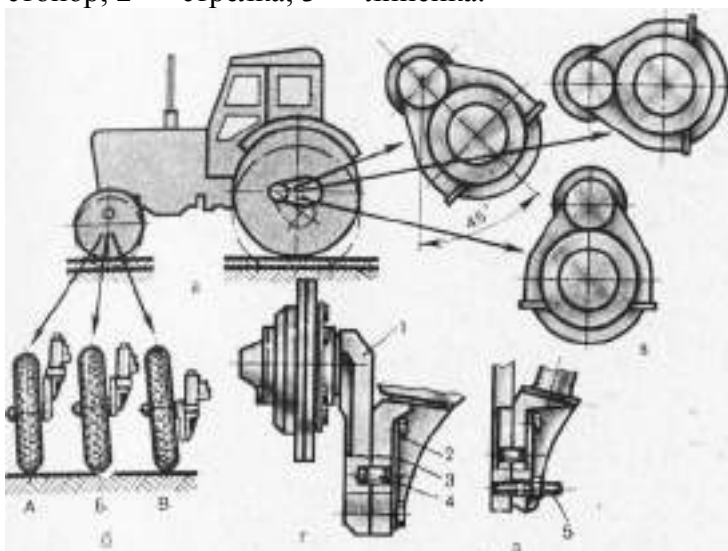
Ходовая часть универсально-пропашного трактора: а — общий вид; б — возможные положения переднего колеса; в — возможные положения конечных передач; г — крепление цапфы переднего колеса трактора Т-40 М; д — то же; Т-25А; 1 — ось; 2 — болт; 3 — замковая шайба; 4 — установочный штифт; 5 — шпилька; А, Б и В — положения цапфы.
